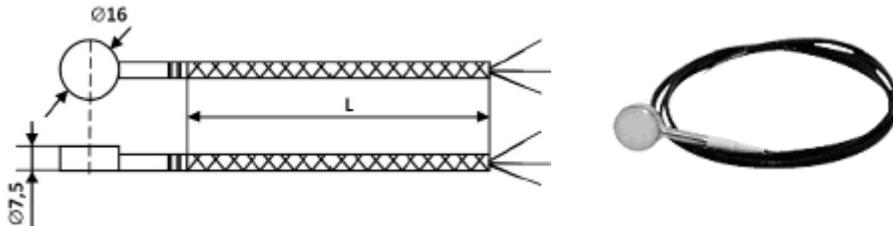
Внешний вид и габаритные размеры термопреобразователя
